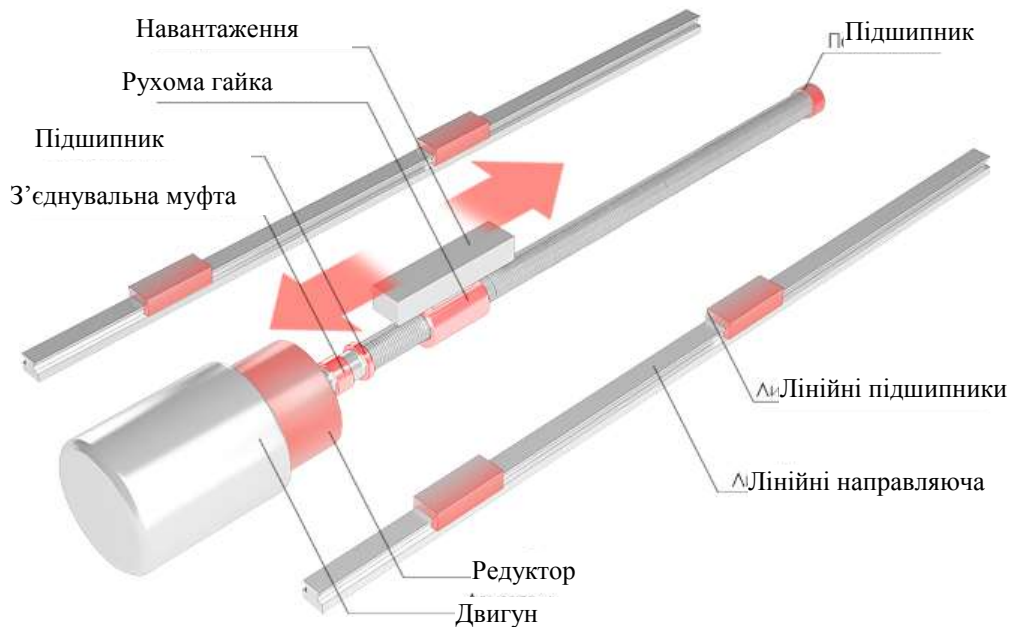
Загальний вигляд сервопривода заслінки рухомої
